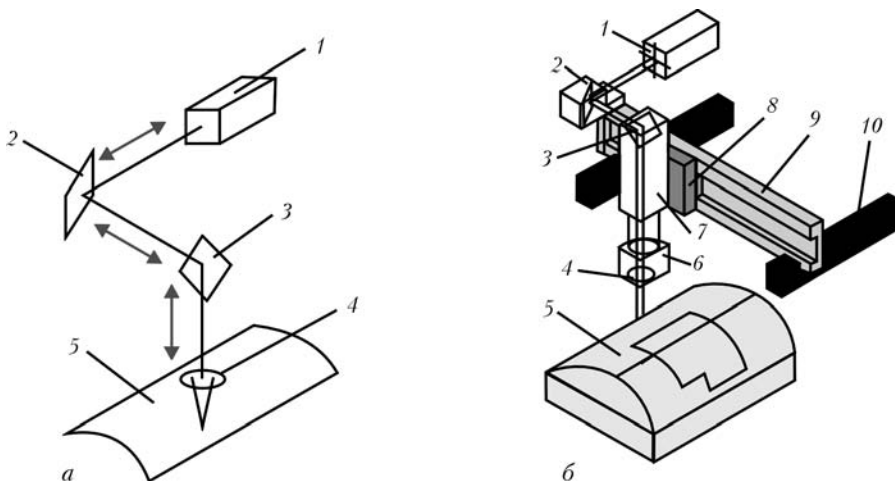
Координатна (а) і конструкційна (б) компоновки 3-координатного ЛТО: 1 – випромінювач лазера; 2, 3 – дзеркала поворотні; 4 – лінза; 5 – заготовка; 6–9 – блоки рухомі; 10 – напрямні
